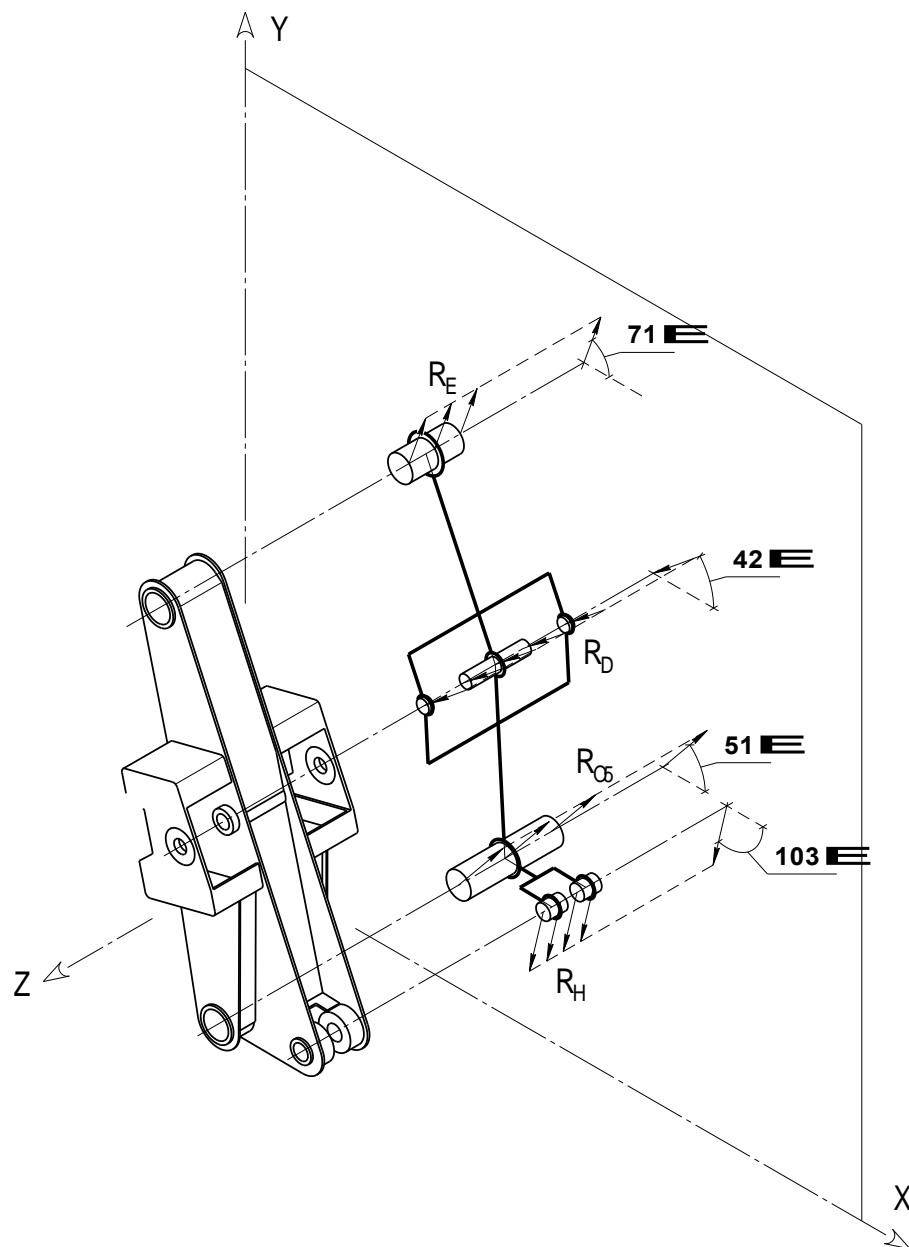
Розрахункова схема вузла «Стріла поворотна»
